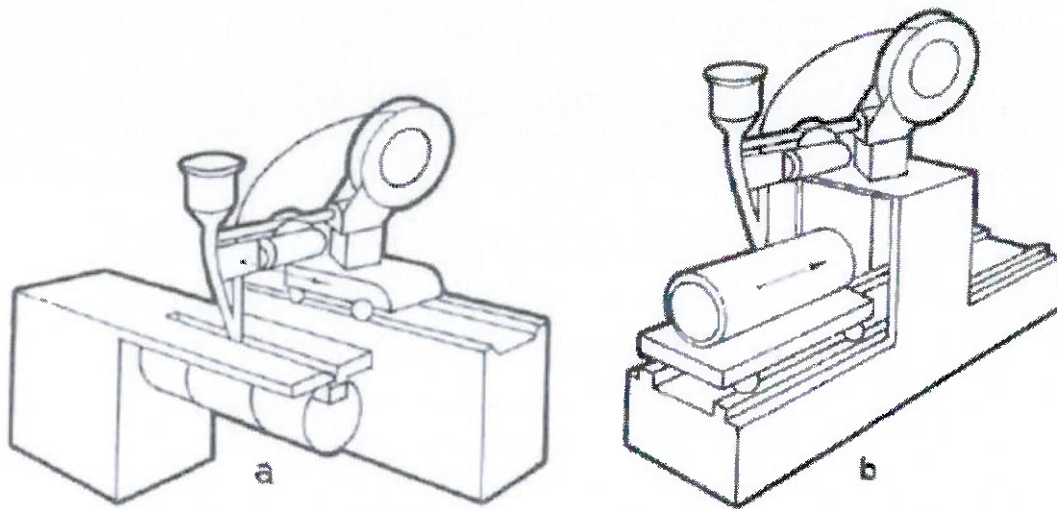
Soldagem em peças circulares. (a) cabeçote se movimentando e (b) cabeçote fixo (Paranhas, 1992)
